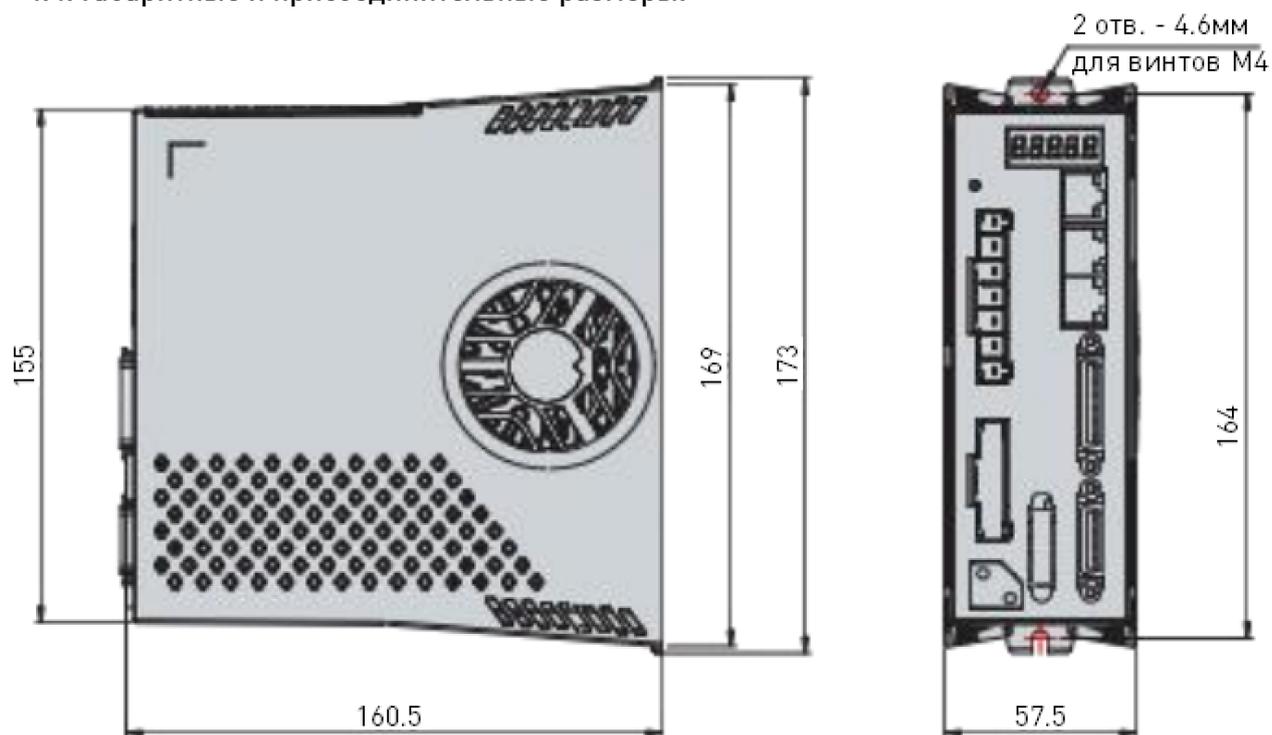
Габаритный чертеж драйверов ETD-A2004/ETD-A2006.
